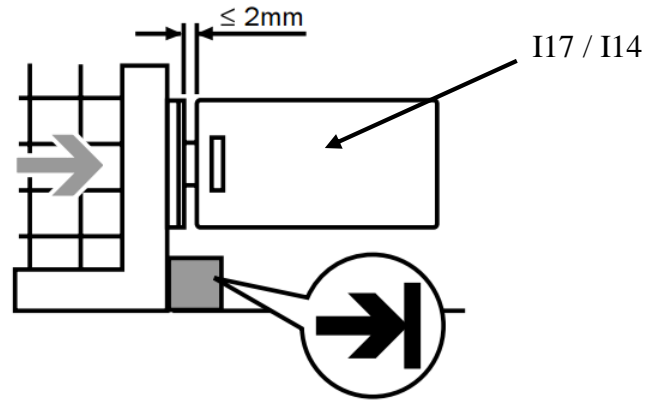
Montagem do dispositivo de segurança I17 ou I14
